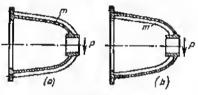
Pieze tipo armazón: reformada con nervios exteriores;
